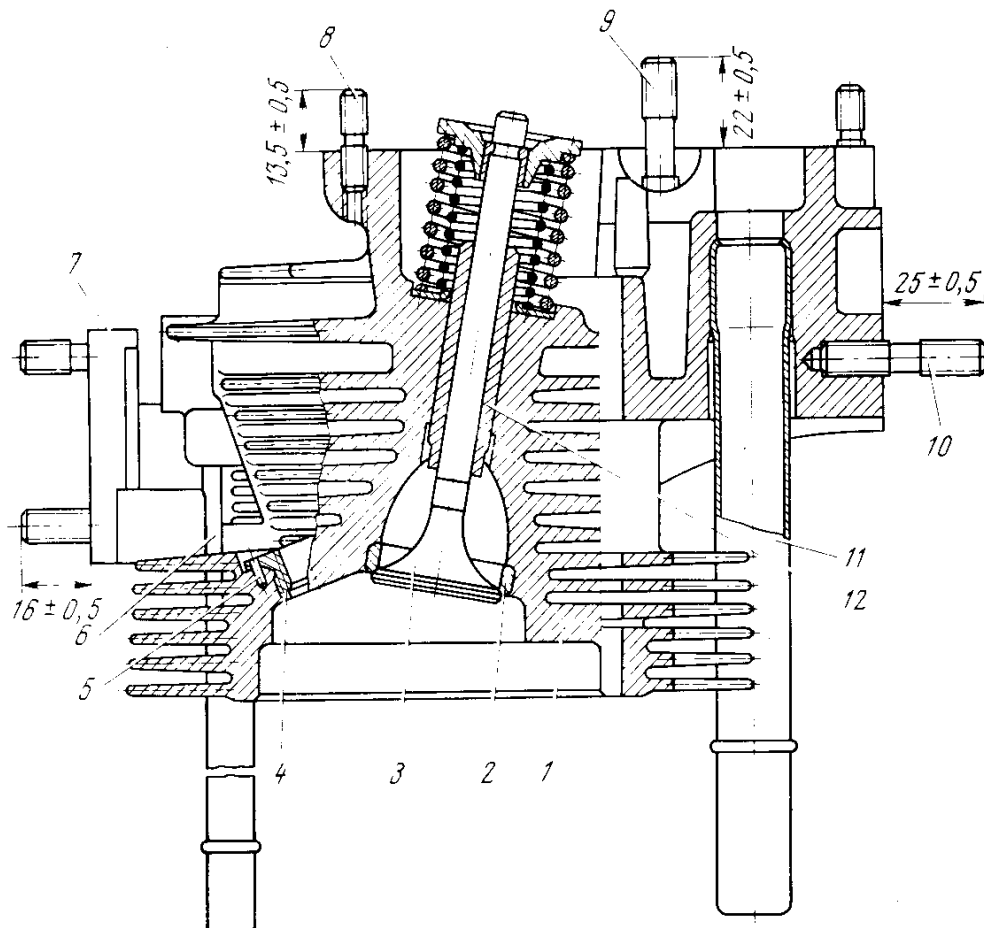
Головка цилиндров с клапанами в сборе: 1 — головка цилиндров; 2 — седло клапана; 3 — клапан; 4 — вставное гнездо свечи; 5 — штифт вставного гнезда свечи; 6 — сливная трубка; 7 — выпускной патрубок с фланцем; 8 — шпилька крепления крышки головки цилиндров; 9 — шпилька крепления валика коромысел; 10 — шпилька крепления впускной трубы; 11 — кожух штанги; 12 — направляющая втулка клапана
